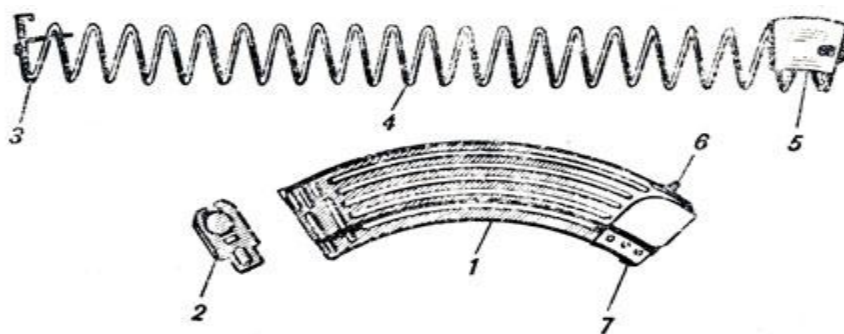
Магазин: 1 - корпус; 2 - крышка; 3 - стопорная планка; 4 - пружина; 5 - подаватель; 6 - опорный выступ; 7 - зацеп
